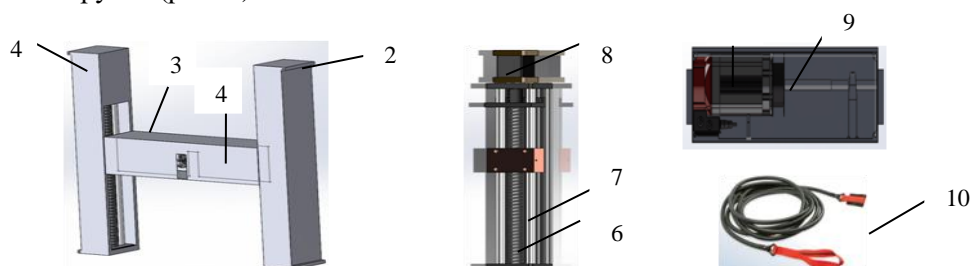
Бросковый тренажер-эспандер для хоккея: 1 – несущие стойки; 2 – крышка несущих стоек; 3 – поперечная балка; 4 – крышка поперечной балки; 5 – винтовой привод с возвратным механизмом SFU1605; 6 – линейные приводы Liner Actuator LA23-10-000A; 7 – каретка; 8 – электродвигатели AC Servo Motor SGMAN-04AAA61D-OY; 9 – катушка; 10 – динамический трос
